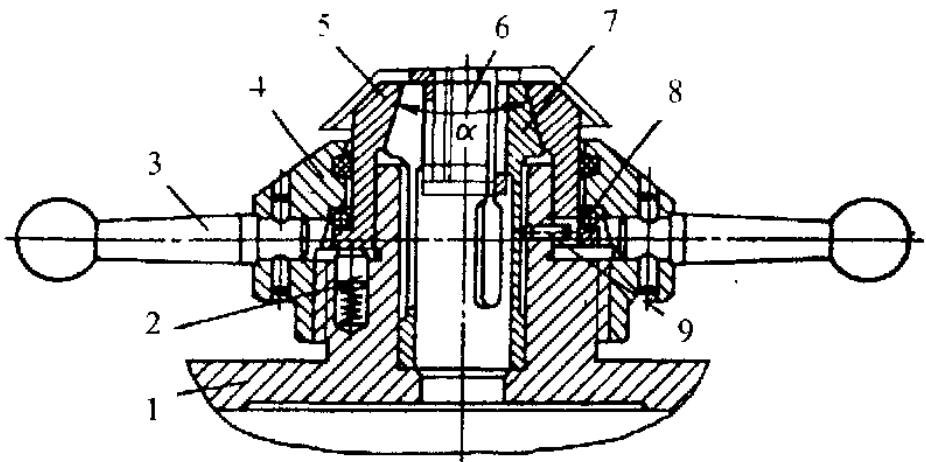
Цанговий механізм, який центрує деталь по зовнішній поверхні
